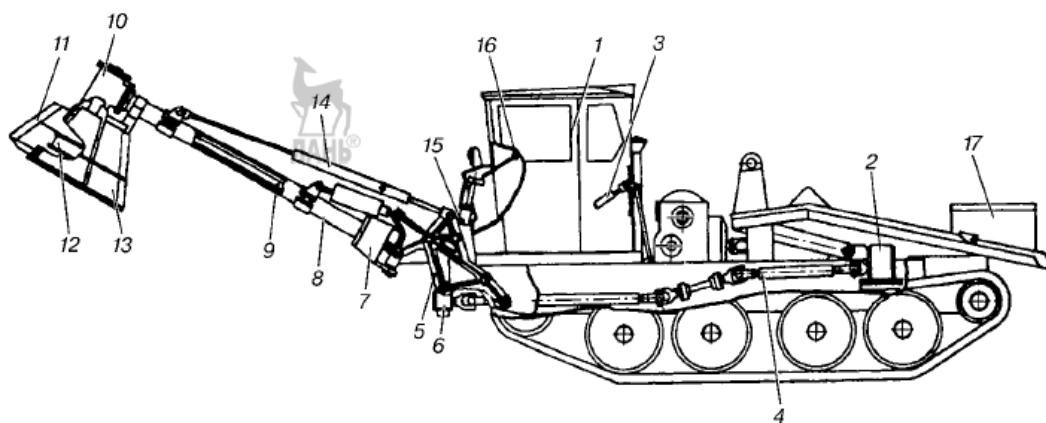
Конструктивная схема машины для удаления пней МУП-4:
